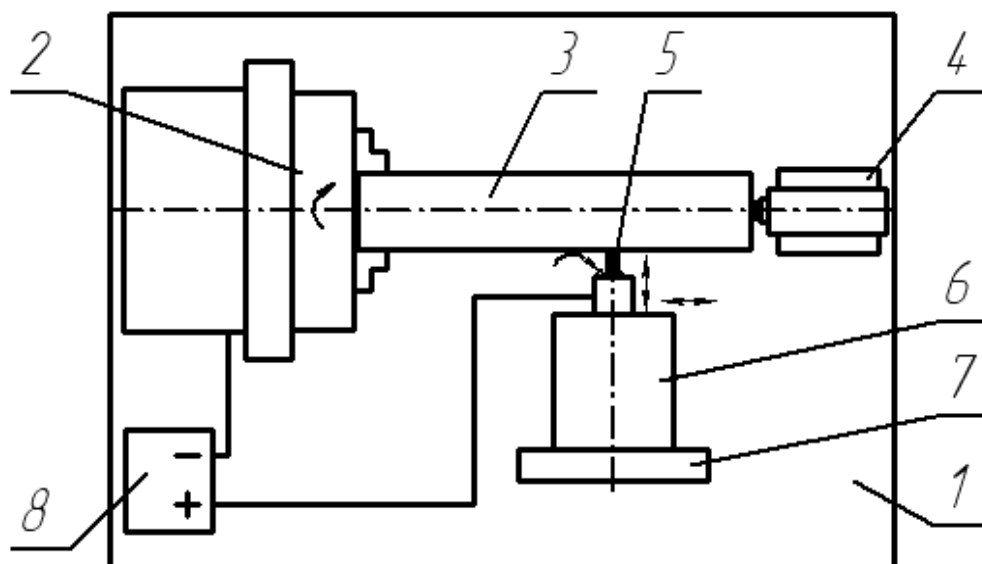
Схема установки для механизированной ЭИО: 1 – база токарного станка; 2 – изолированный кулачковый патрон; 3 – обрабатываемая деталь; 4 – изолированная задняя бабка; 5 – легирующий электрод; 6 – механизированная головка с суппортом станка; 7 – следящая система; 8 – генератор импульсов
